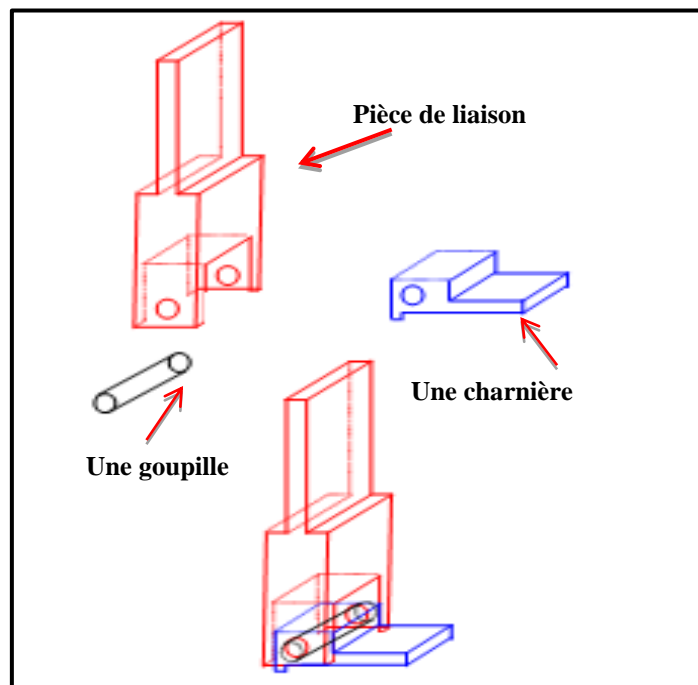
Schéma du dispositif de fixation de l'éprouvette à la machine.
